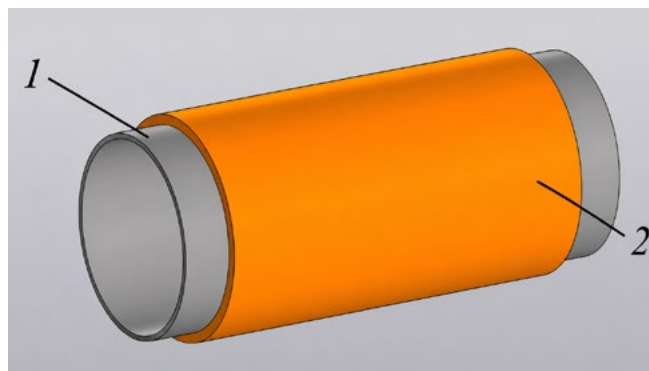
Стеклопластиковый бандаж на трубопроводе:
